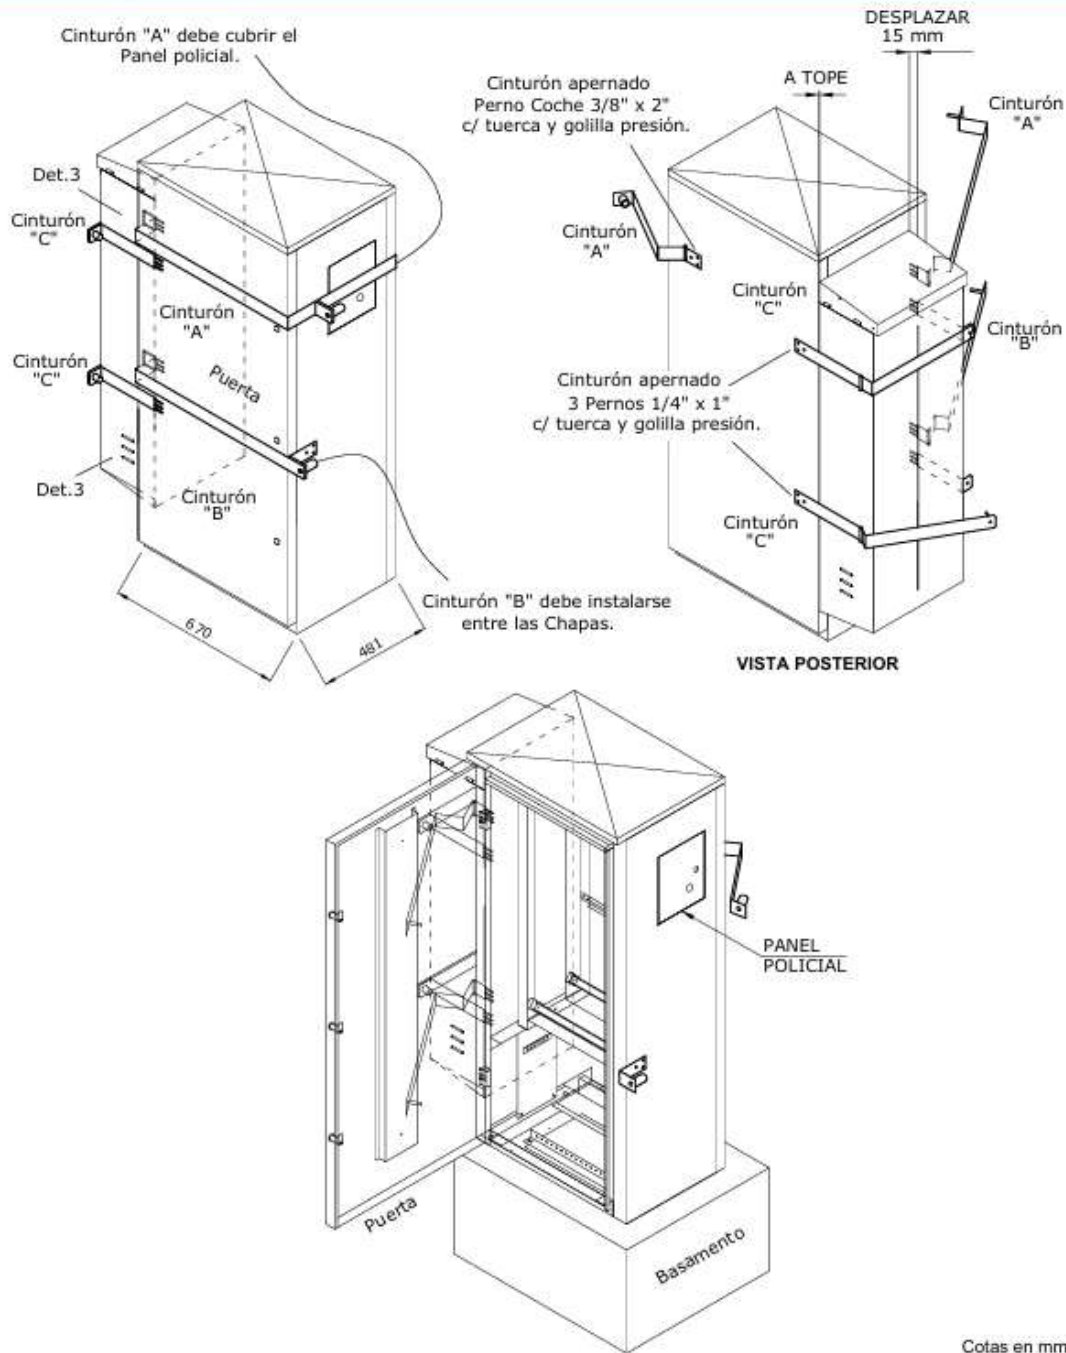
66 Refuerzo para Puerta de Gabinete de Control
